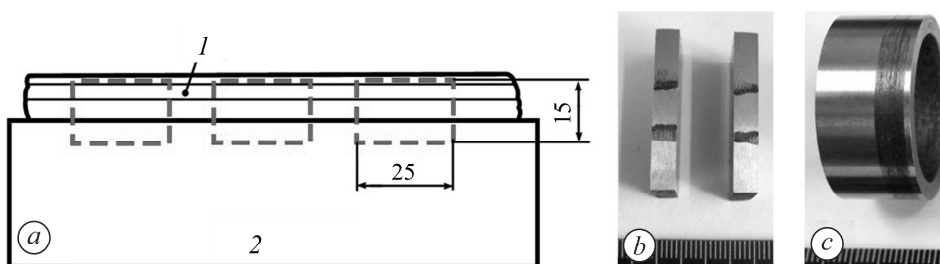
Схема вирізання зразків із наплавленого металу (a) та зовнішній вигляд зразків (b) і контртіла (c) після випробувань на зносотривкість під час тертя металу об метал при 20°C: 1 – наплавлений метал; 2 – основний.
